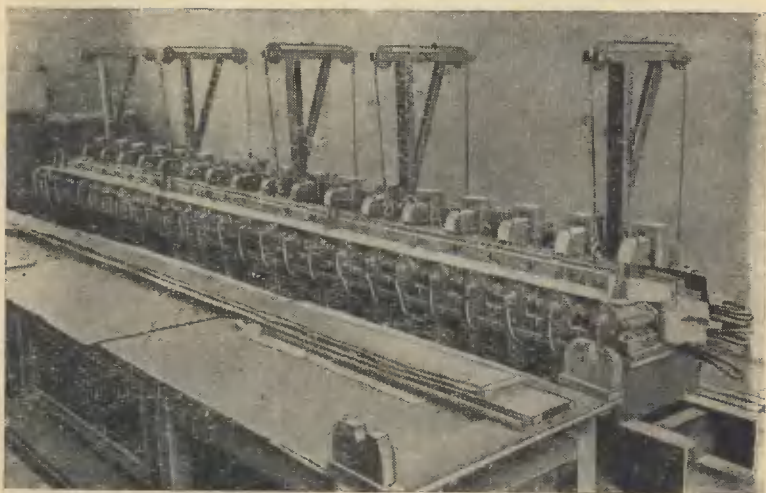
Прессформа для изготовления роторных гильз и витковой изоляции.
